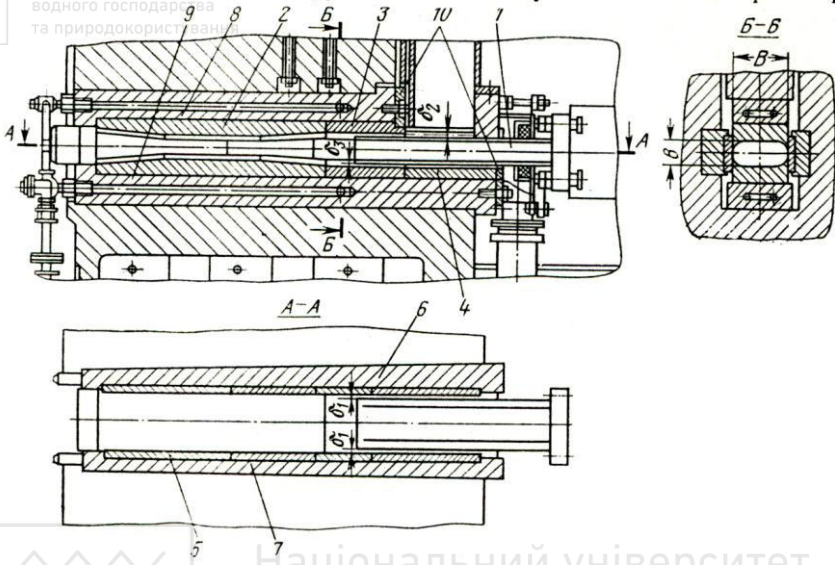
Матричний інструмент штемпельного преса [5, с.512]:
